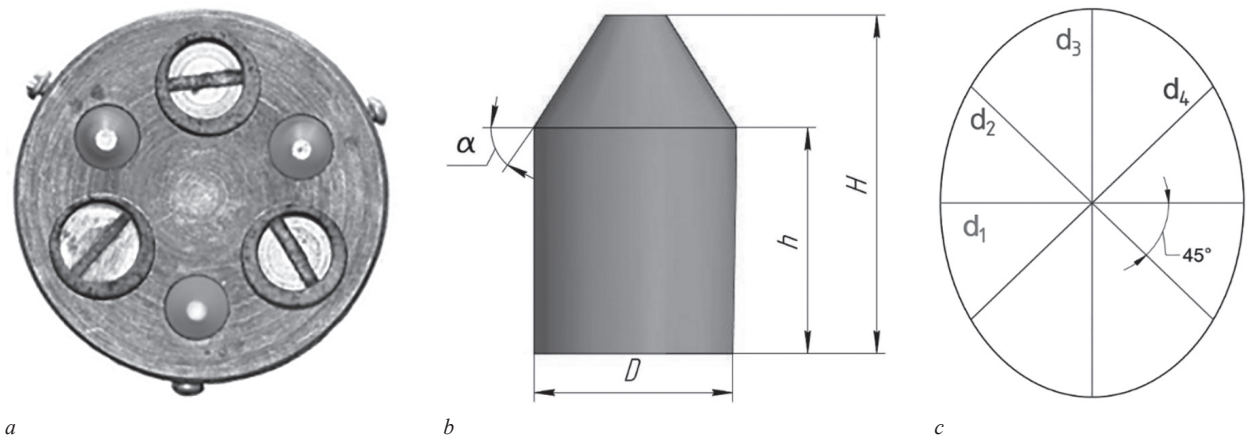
Схема образцов в виде усеченного конуса: *a* — держатель образцов; *b* — испытуемый образец (α — угол у основания конуса, h — высота цилиндрической части, H — высота образца, D — диаметр образца); *c* — схема определения диагоналей пятна износа
